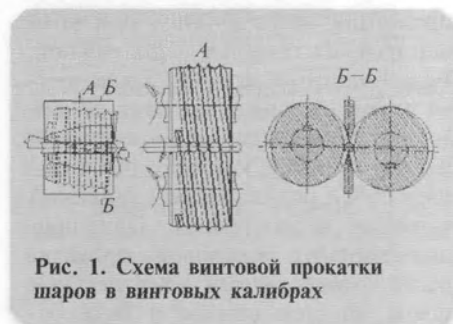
Схема винтовой прокатки шаров в винтовых калибрах
